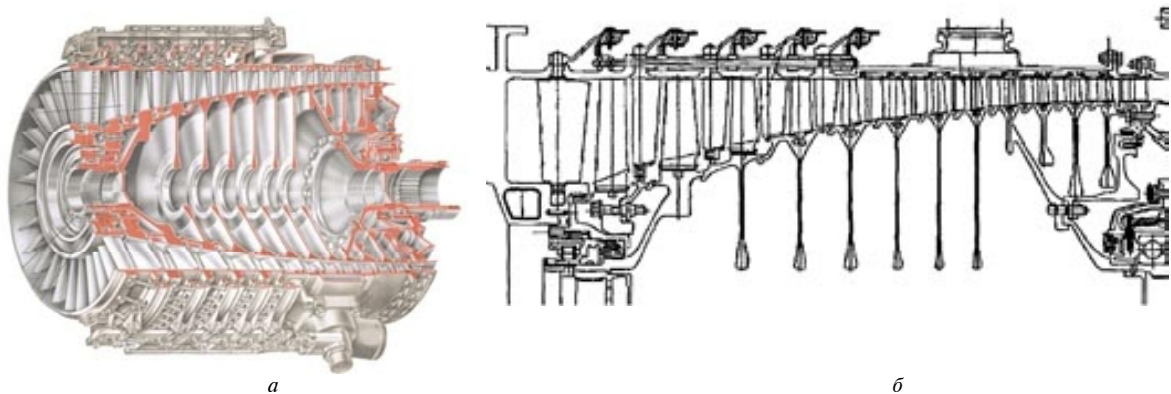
Общий вид (а) и схема (б) компрессора турбовального двигателя ТВ3-117
